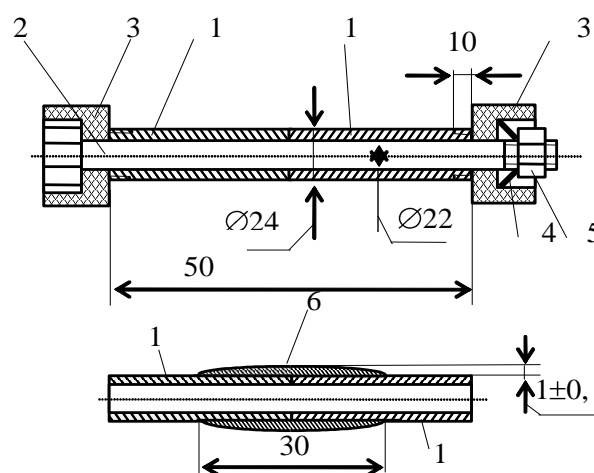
Схема пристрою для нанесення покриття на зразок для визначення когезії покриття за розтягу: 1 – дві частини зразка; 2 – штифт; 3 – захисні шайби; 4 – пружина; 5 – гайка; 6 – покриття.
